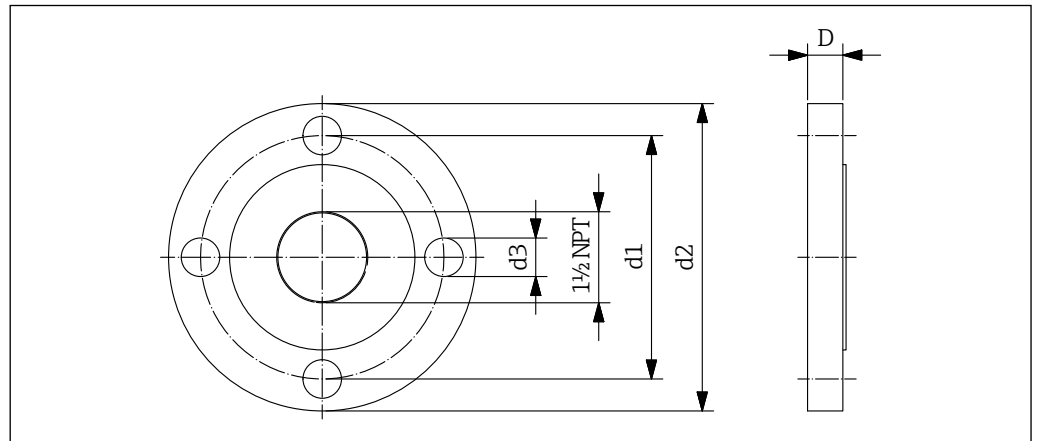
Dimensioni flangia di montaggio (Dimensioni di connessione secondo DIN EN 1092-1)
